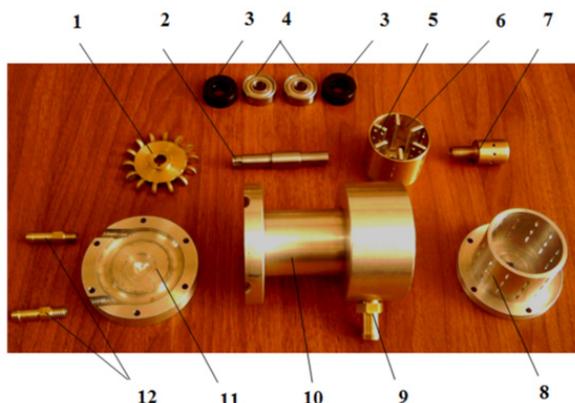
Внешний вид деталей ДА: 1 – крыльчатка; 2 – вал привода; 3 – сальник; 4 – подшипник; 5 – крыльчатка ротора; 6 – ротор; 7 – дополнительный кавитатор; 8 – статор; 9 – штуцер, отводящий; 10 – корпус; 11 – крышка; 12 – штуцеры
